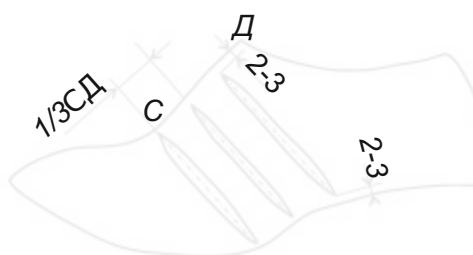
Розтин зліпку бокової поверхні колодки
